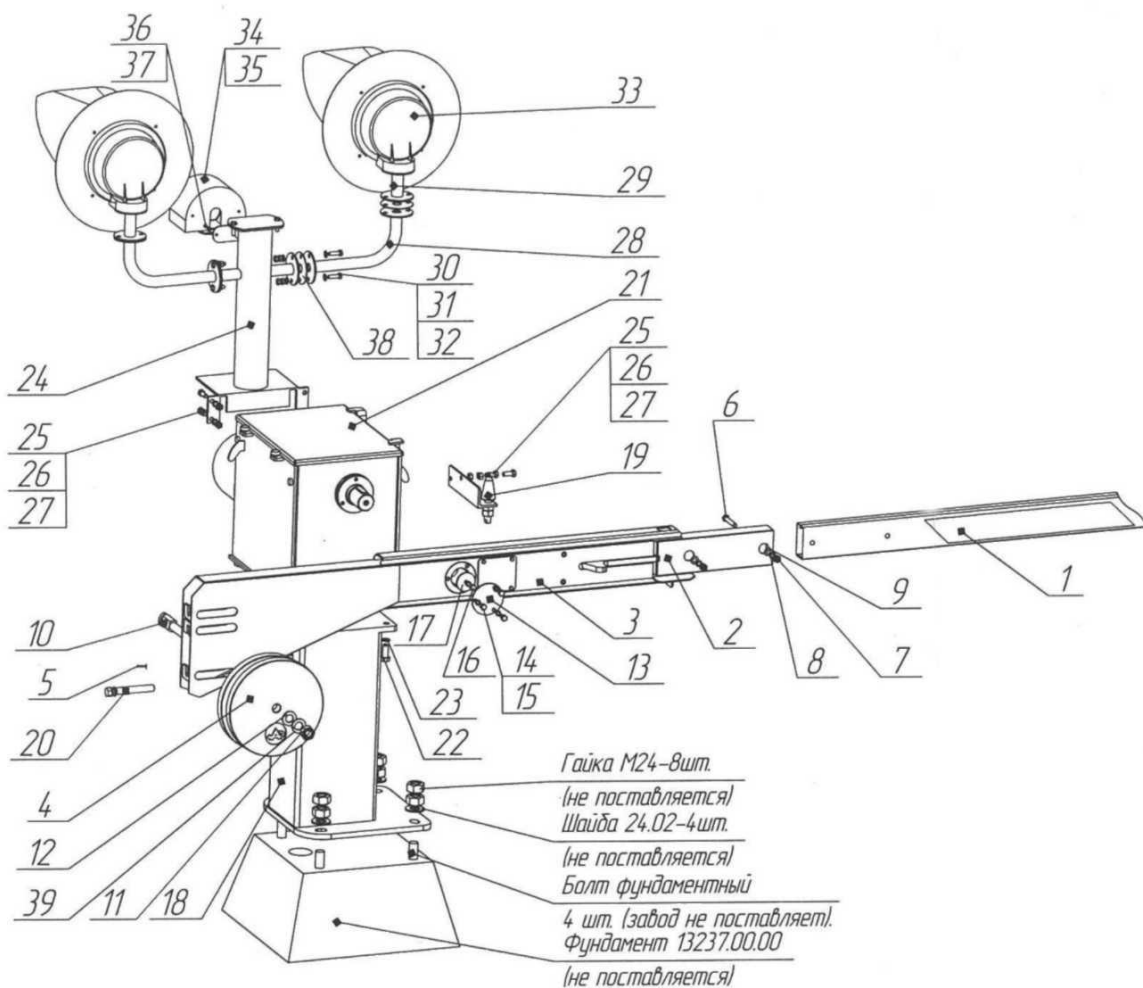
Схема сборки (разборки) шлагбаума ША
